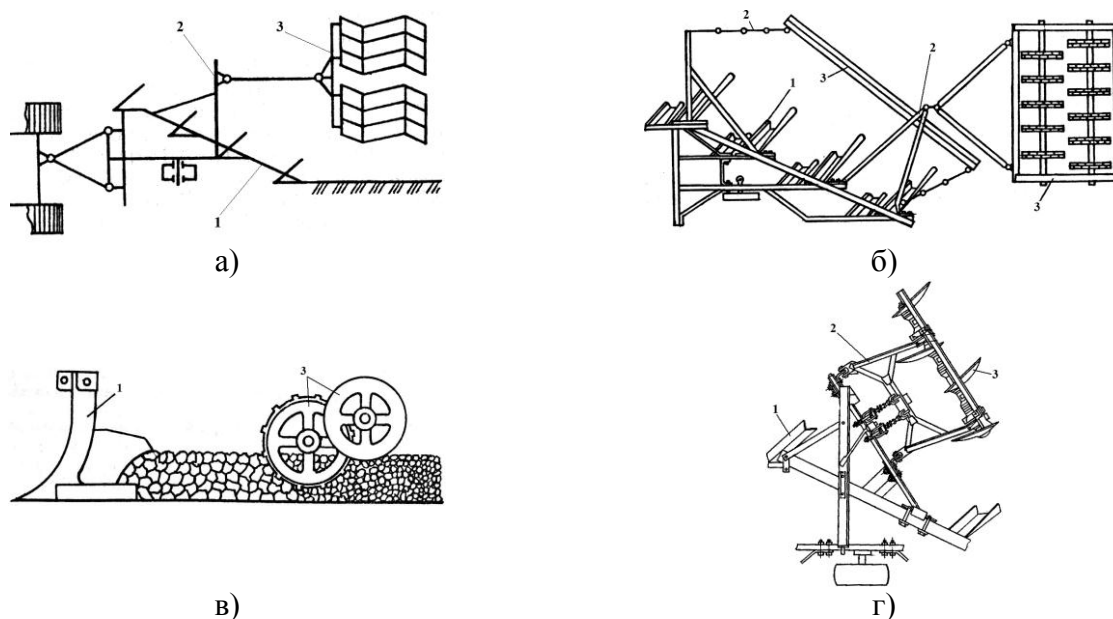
Схемы приспособлений для поверхностной обработки почвенного пласта в конструкциях пахотных агрегатов: а – с использованием зубовых борон, б, в – катковых приставок, г – дисковой секции бороны, 1 – плуг, 2 – прицепное устройство, 3 – дополнительное приспособление
